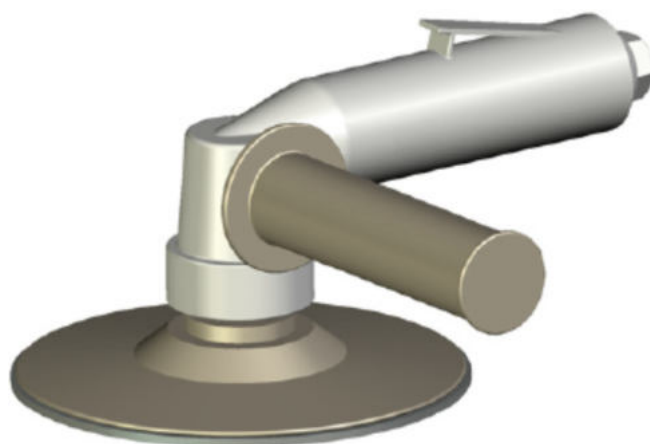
Угловая круглошлифовальная/полировальная машина, в которой в качестве основной рукоятки используется корпус двигателя
